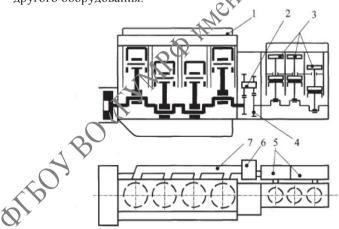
Комбинированная установка поршневого двигателя и двигателя Стирлинга:
